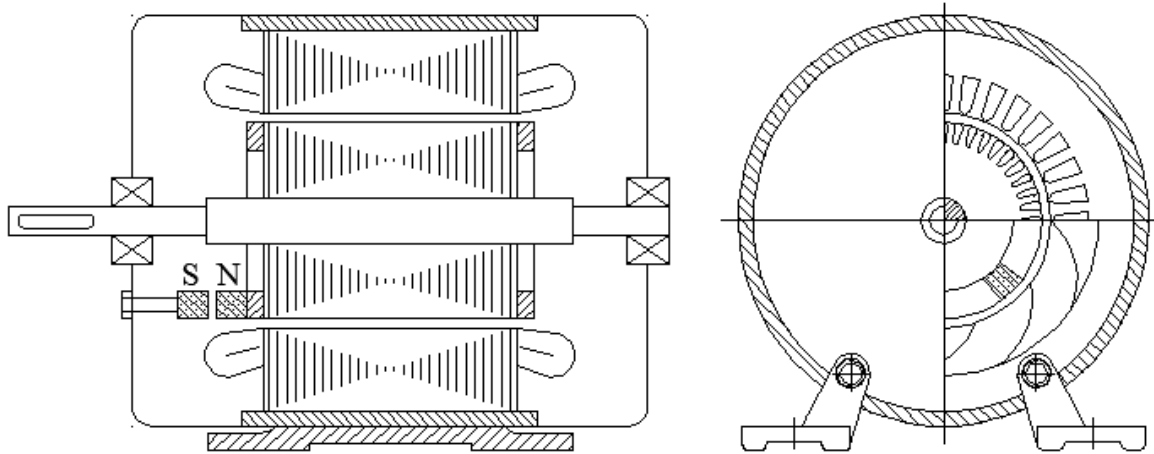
Explicativă la montarea dispozitivului de oprire și fixarea rotorului în poziția necesară
